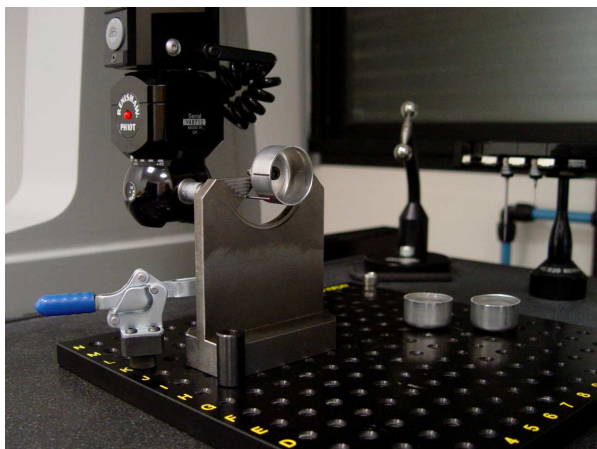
Machine à mesurer tridimensionnelle.
